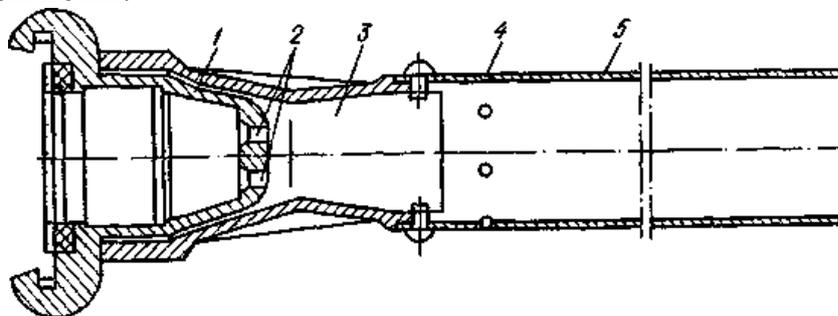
Ствол воздушно-пенный СВП: 1 – корпус ствола; 2 – отверстия; 3 – конусная камера; 4 – отверстия в кожухе; 5 – кожух
